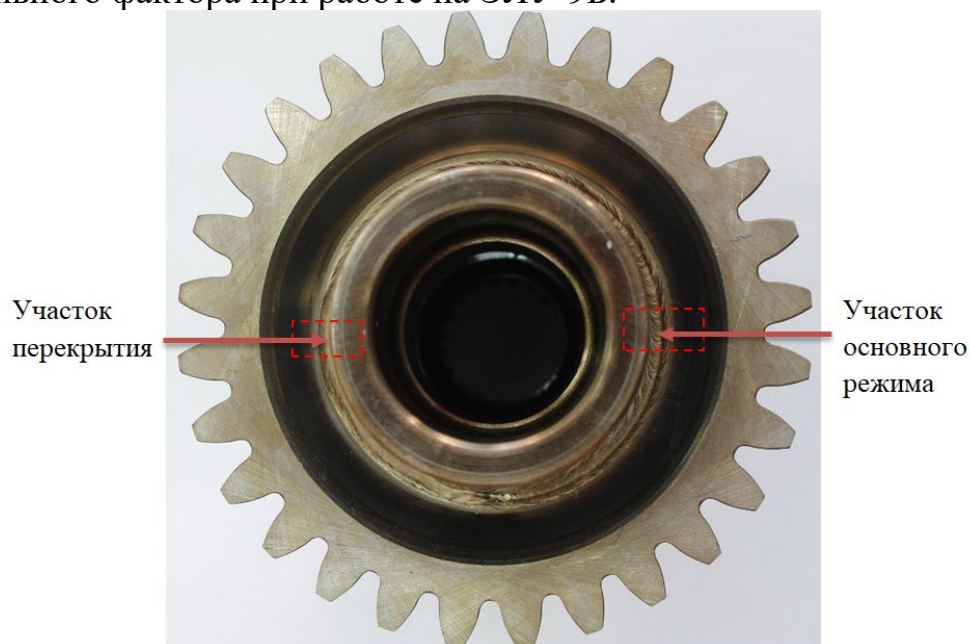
Шлифы образца-свидетеля зубчатого колеса:
